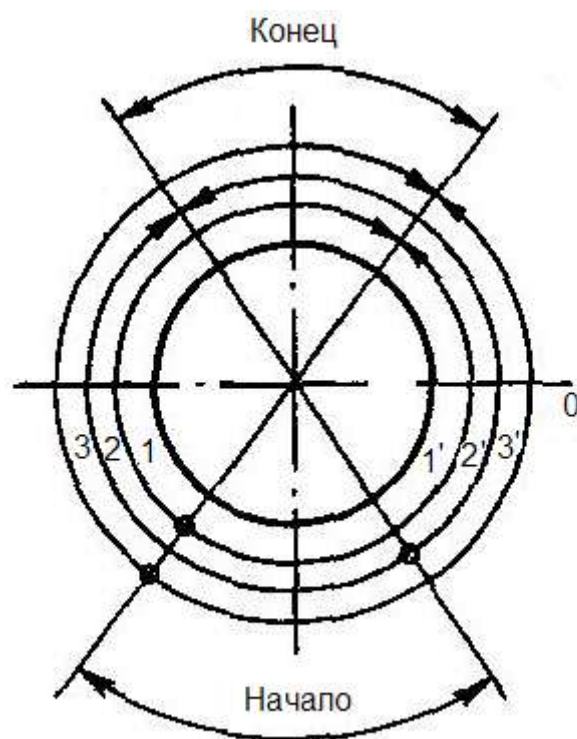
Сварка неповоротных стыков газопроводов.
